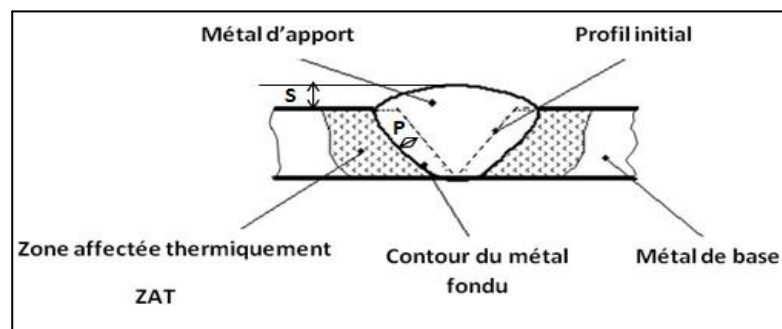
constituants d'un assemblage soudé.
